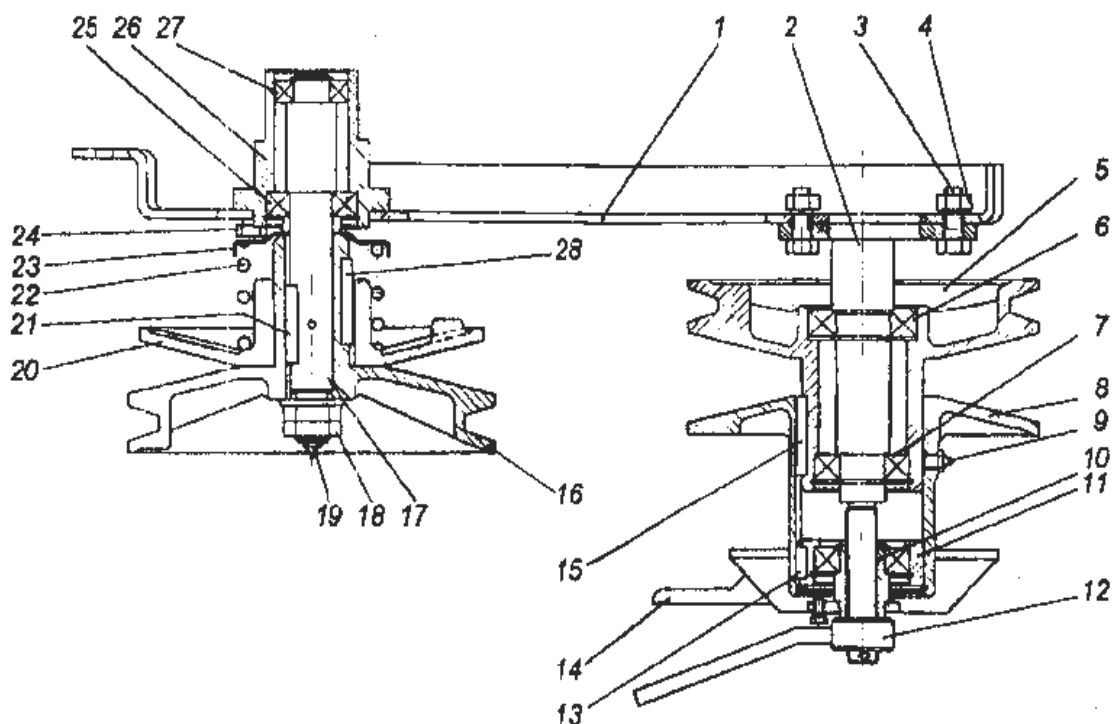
Вариатор вентилятора: 1 – плита; 2 – ось; 3, 24 – болты; 4 – гайка; 5 – диск неподвижный ведущего блока; 6, 7, 25, 27 – шарикоподшипники; 8 – диск подвижный ведущего, блока; 9, 19 – масленки; 10 – резьбовая втулка; 11 – подшипниковый узел; 12 – стопорная гайка; 13, 15, 21, 28 – шпонки призматические; 14 – штурвал; 16 – диск неподвижный ведомого блока; 17 – вал; 18 – гайка; 20 – диск подвижный ведомого блока; 22 – пружина; 23 – шайба; 26 – корпус
